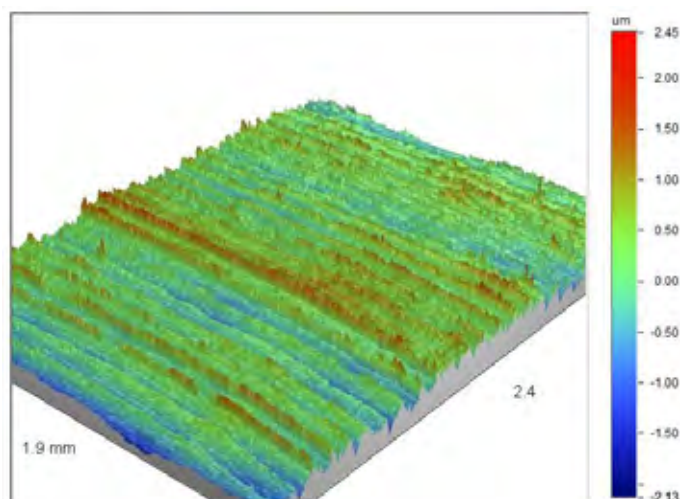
Representação tridimensional da superfície do material CR, usinado sob condição C3.
